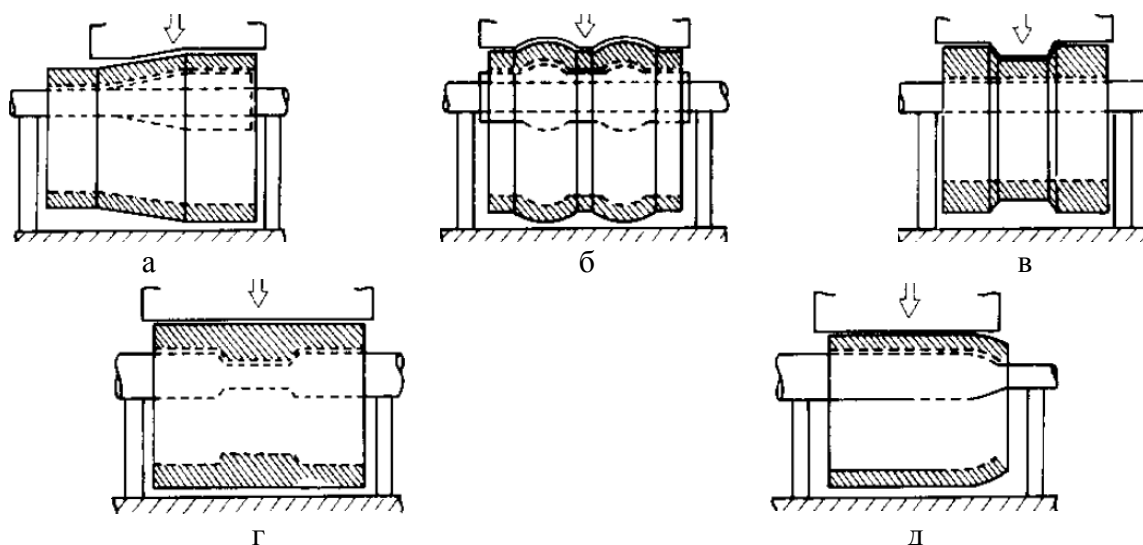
Способыковки поковки со ступенчатой формой поперечного сечения, предложенные JSW
